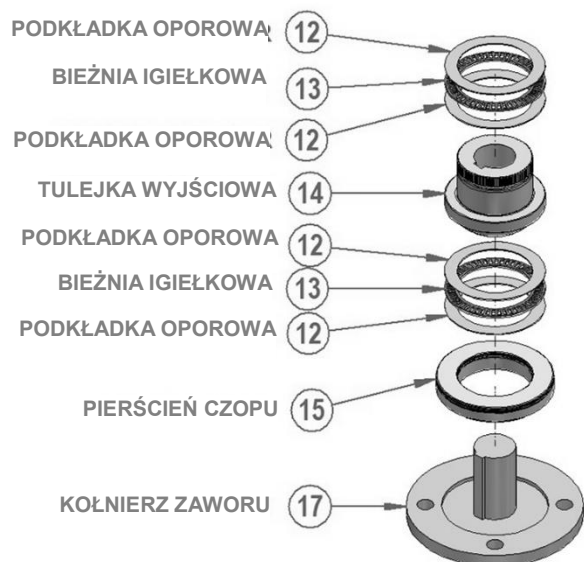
Uszczelnienie kołnierza montażowego zaworu
